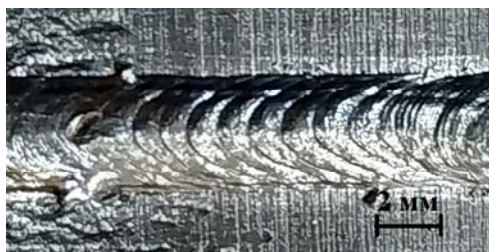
Внешний вид валика при наплавке с круговой разверткой электронного луча
